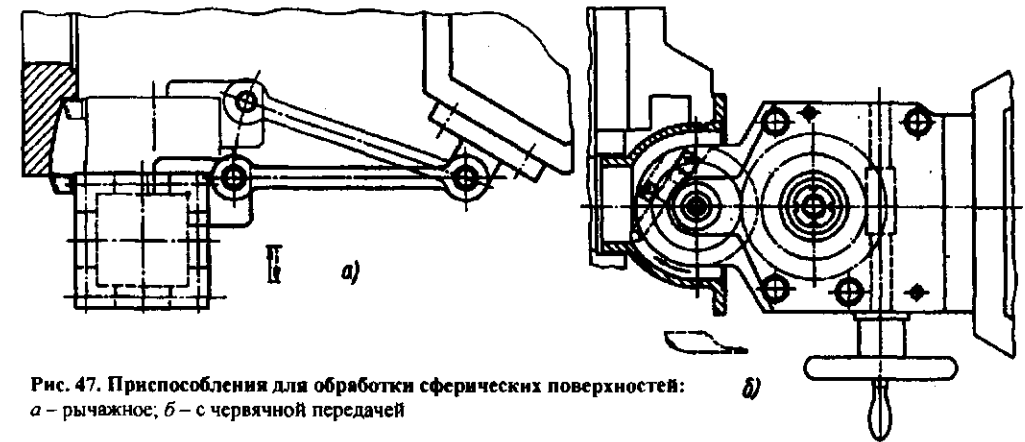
Приспособления для обработки сферических поверхностей: а – рычажное; б – с червячной передачей
